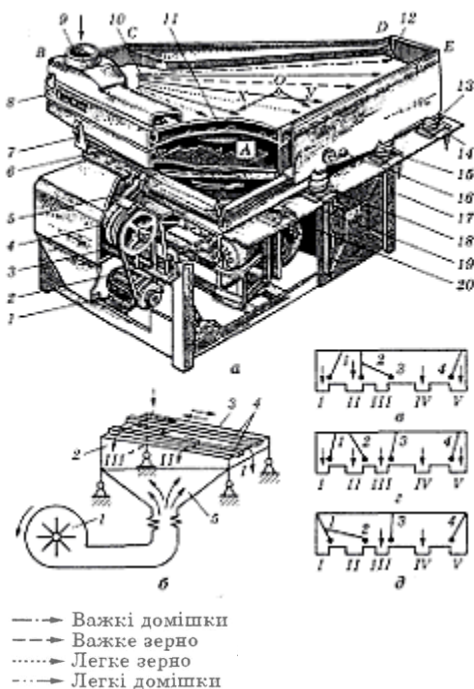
Пневматичний сортувальний стіл ПСС-2,5В:
